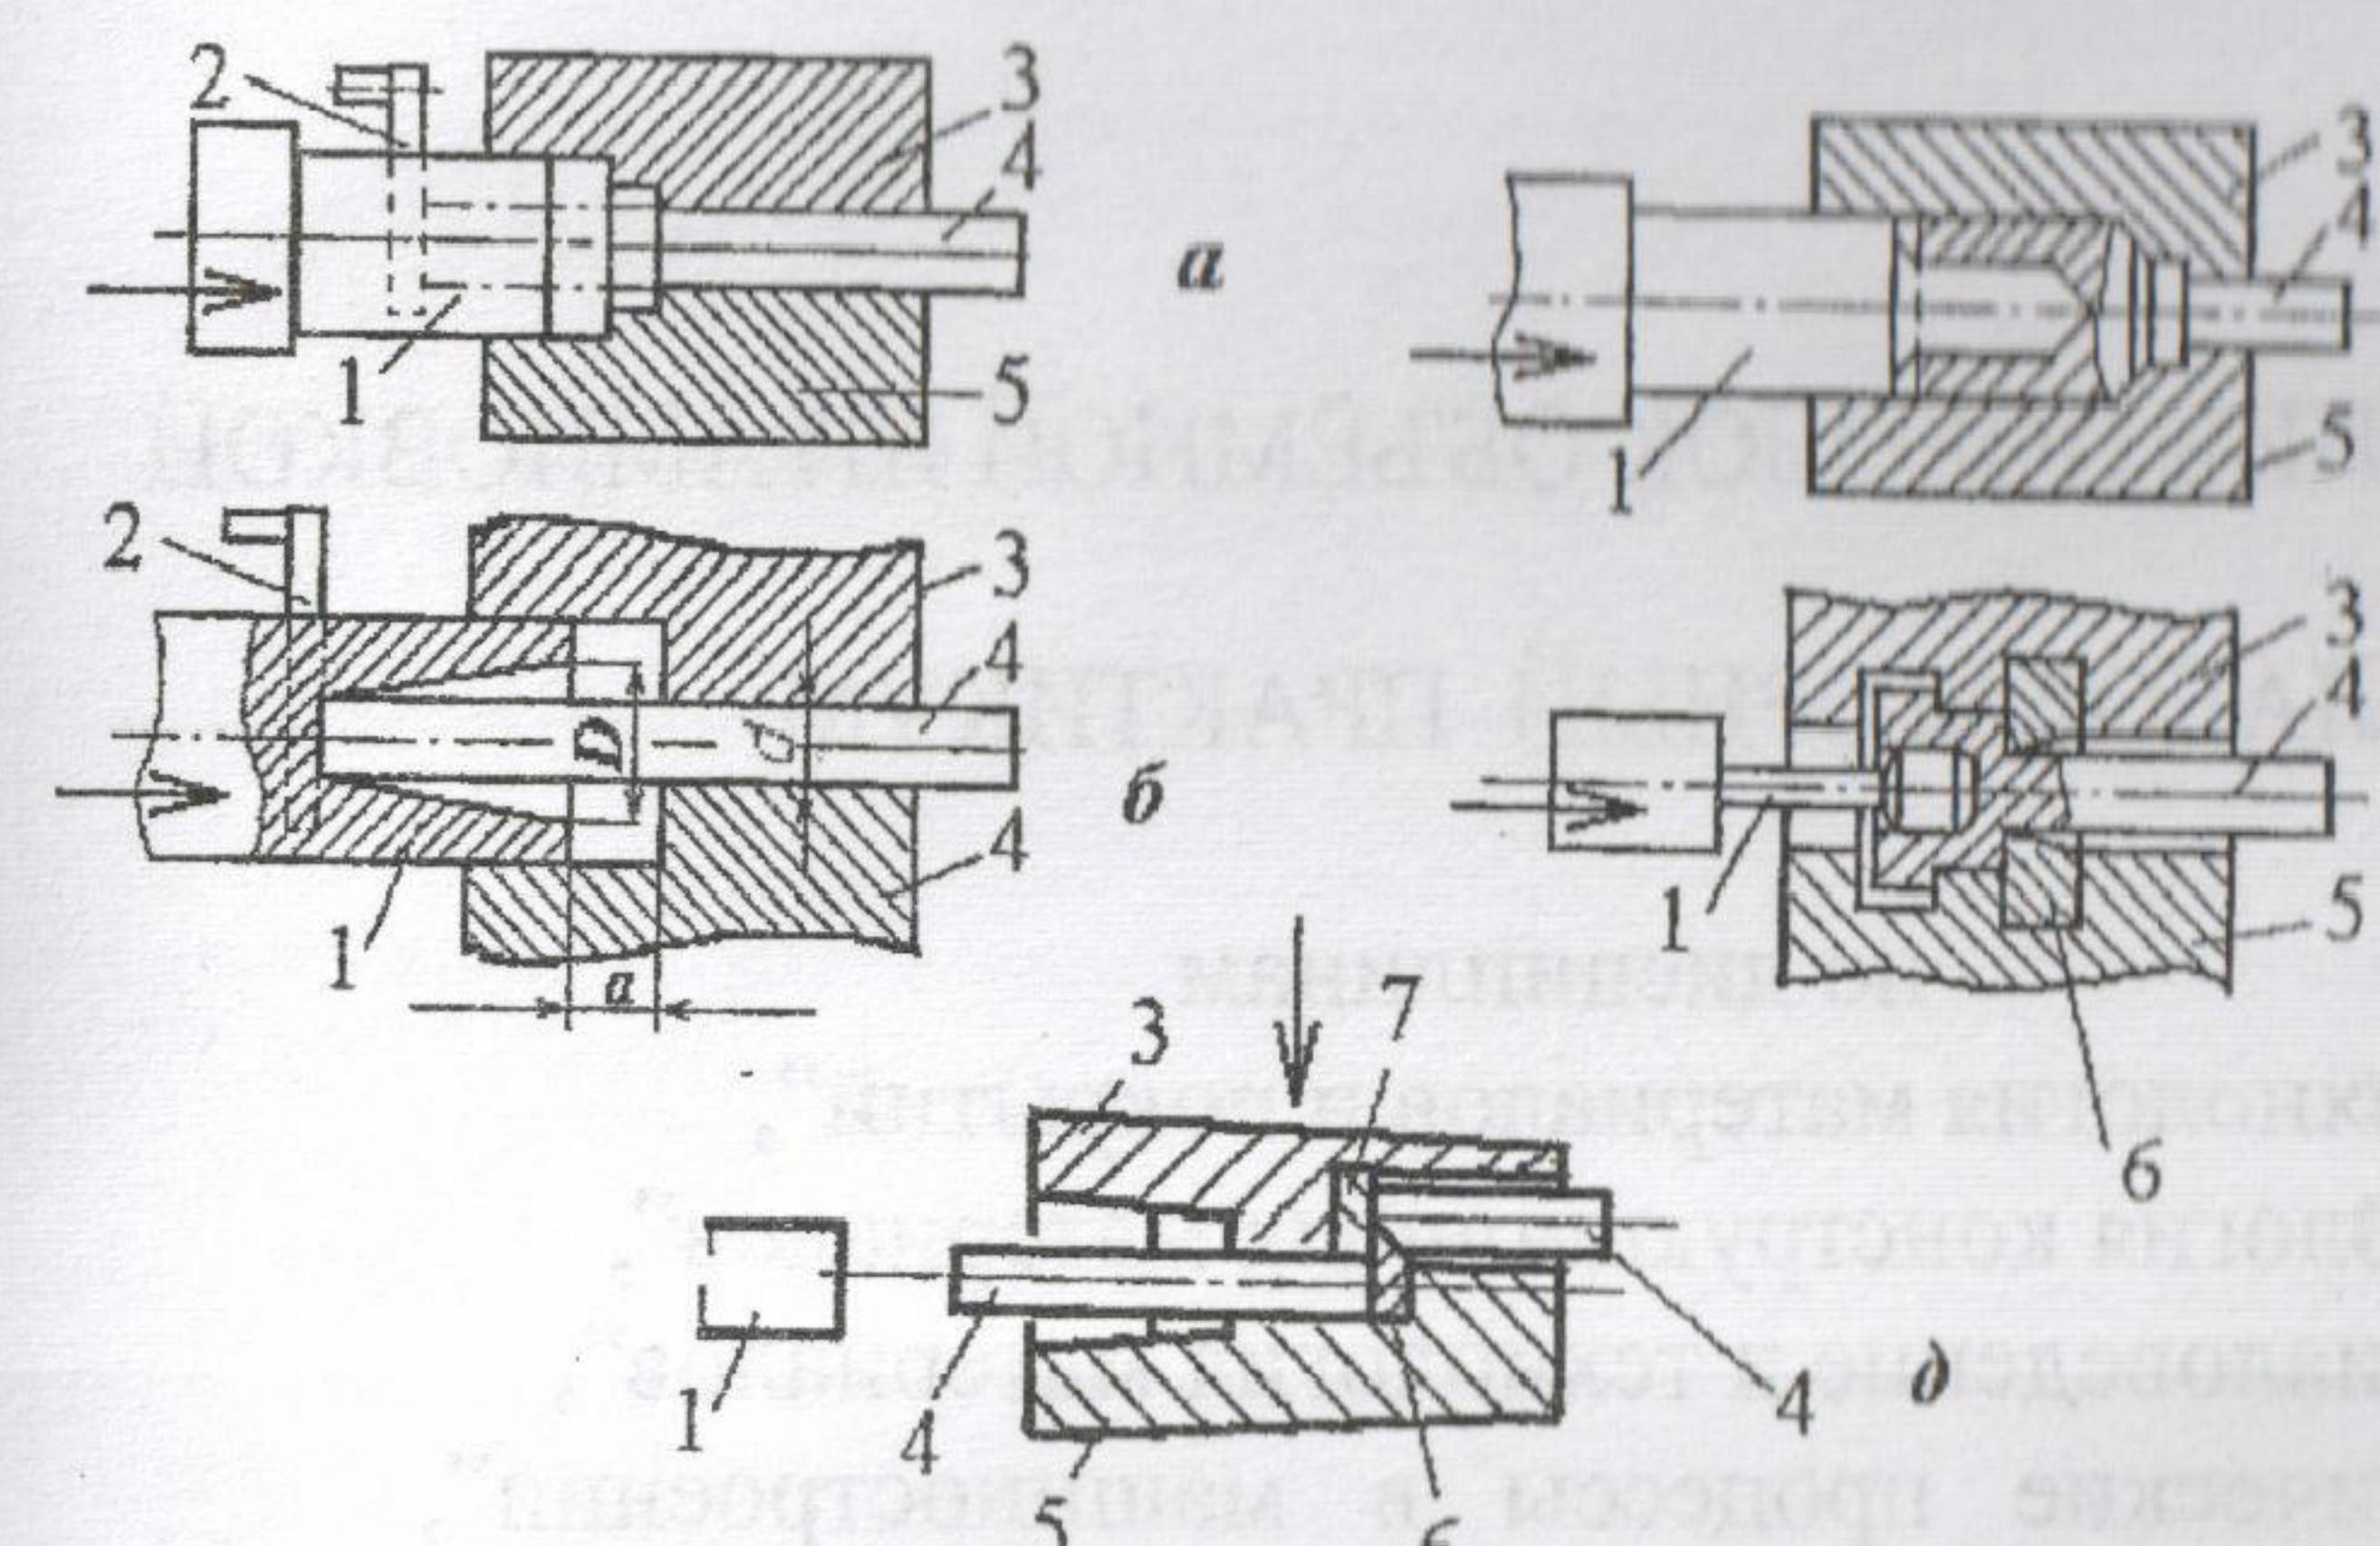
П3. Основные операции, выполняемые на ГКМ: а, б – высадка; в – прошивка; г – пробивка; д – отрезка
